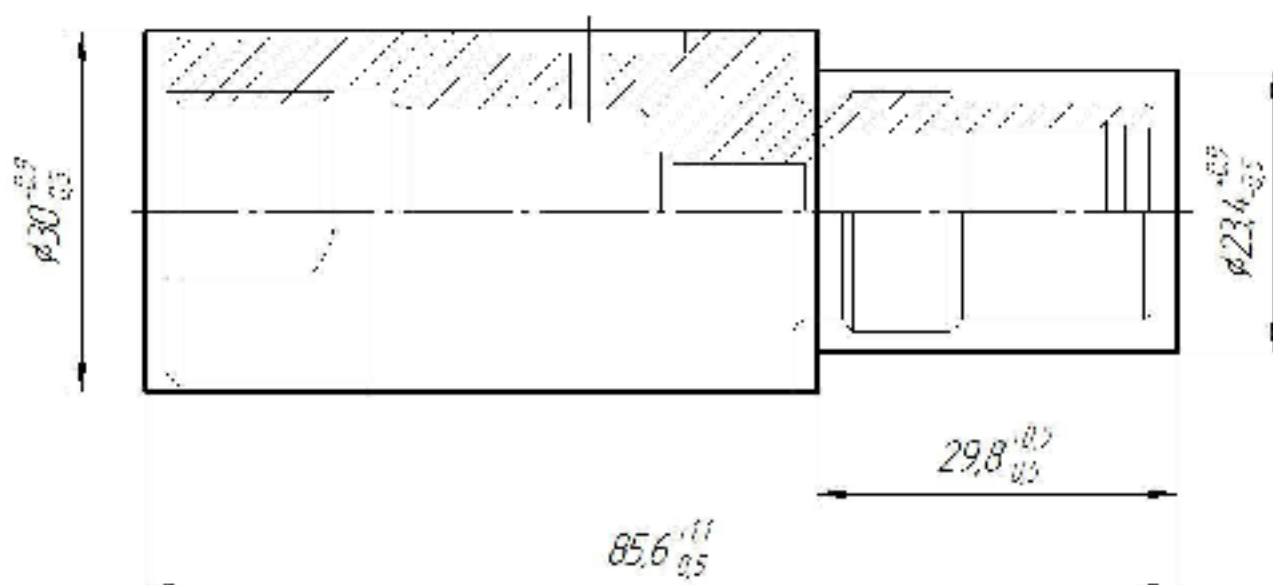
Ескіз заготовки при штампуванні на КГШП
